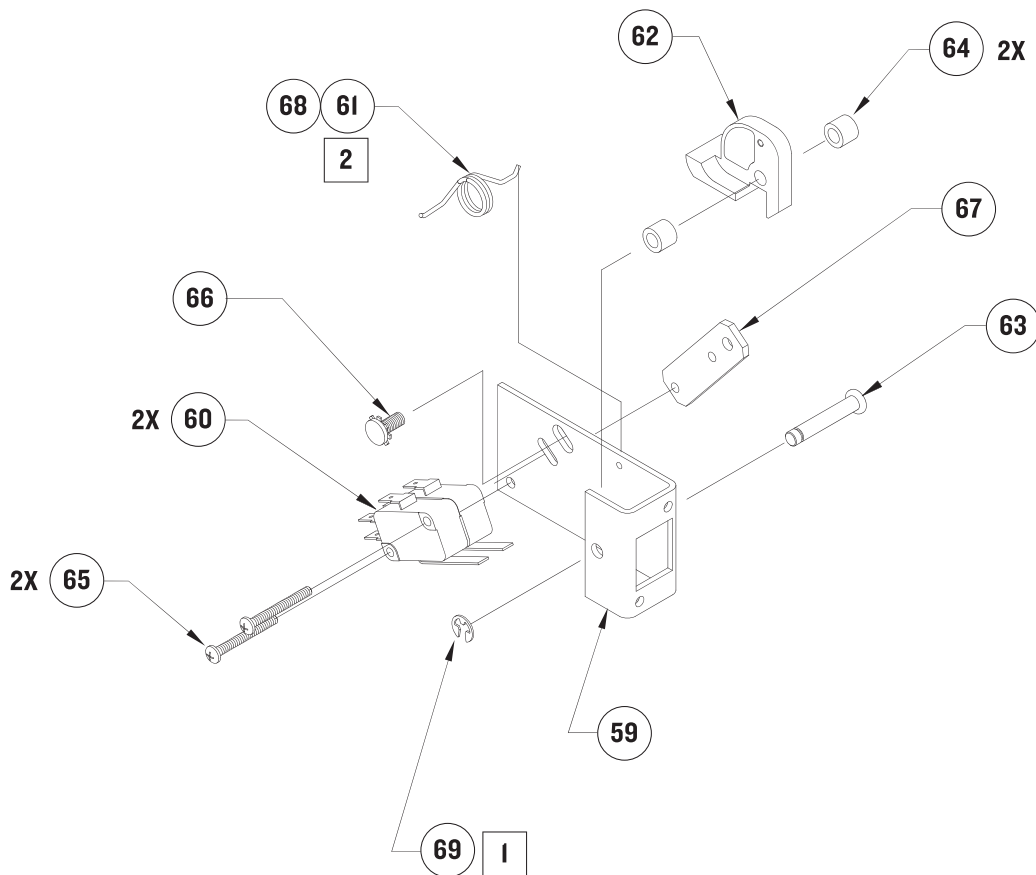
Conjunto y piezas del interruptor de la puerta
